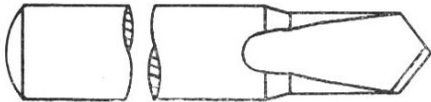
Der Bohrer zum Ausbohren des Schraubenstumpfes
